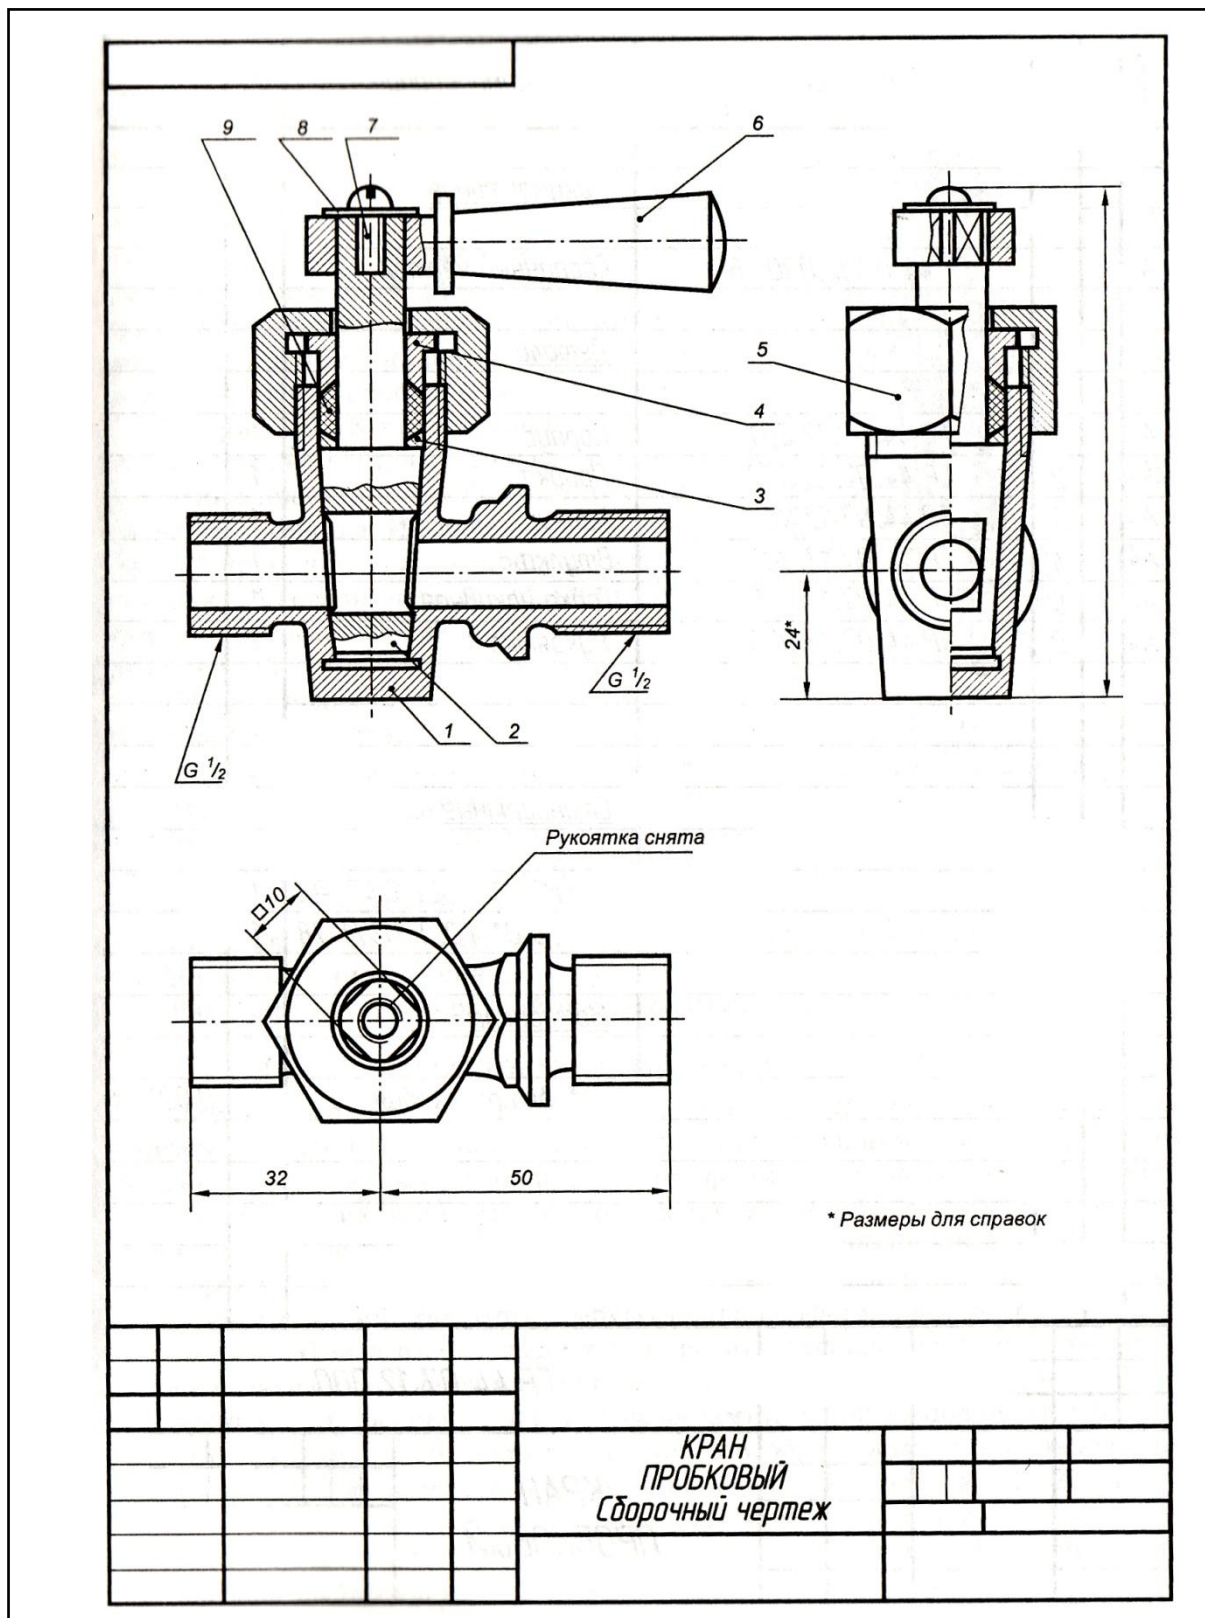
Сборочный чертеж «Кран пробковый»
